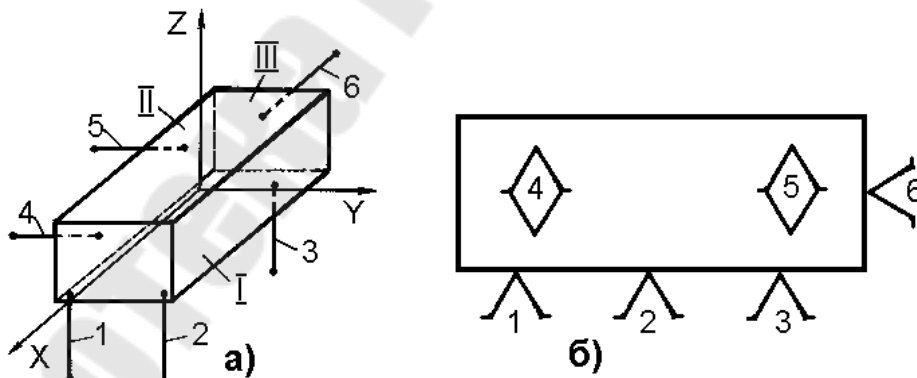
Опорные точки и схема базирования призматической заготовки
